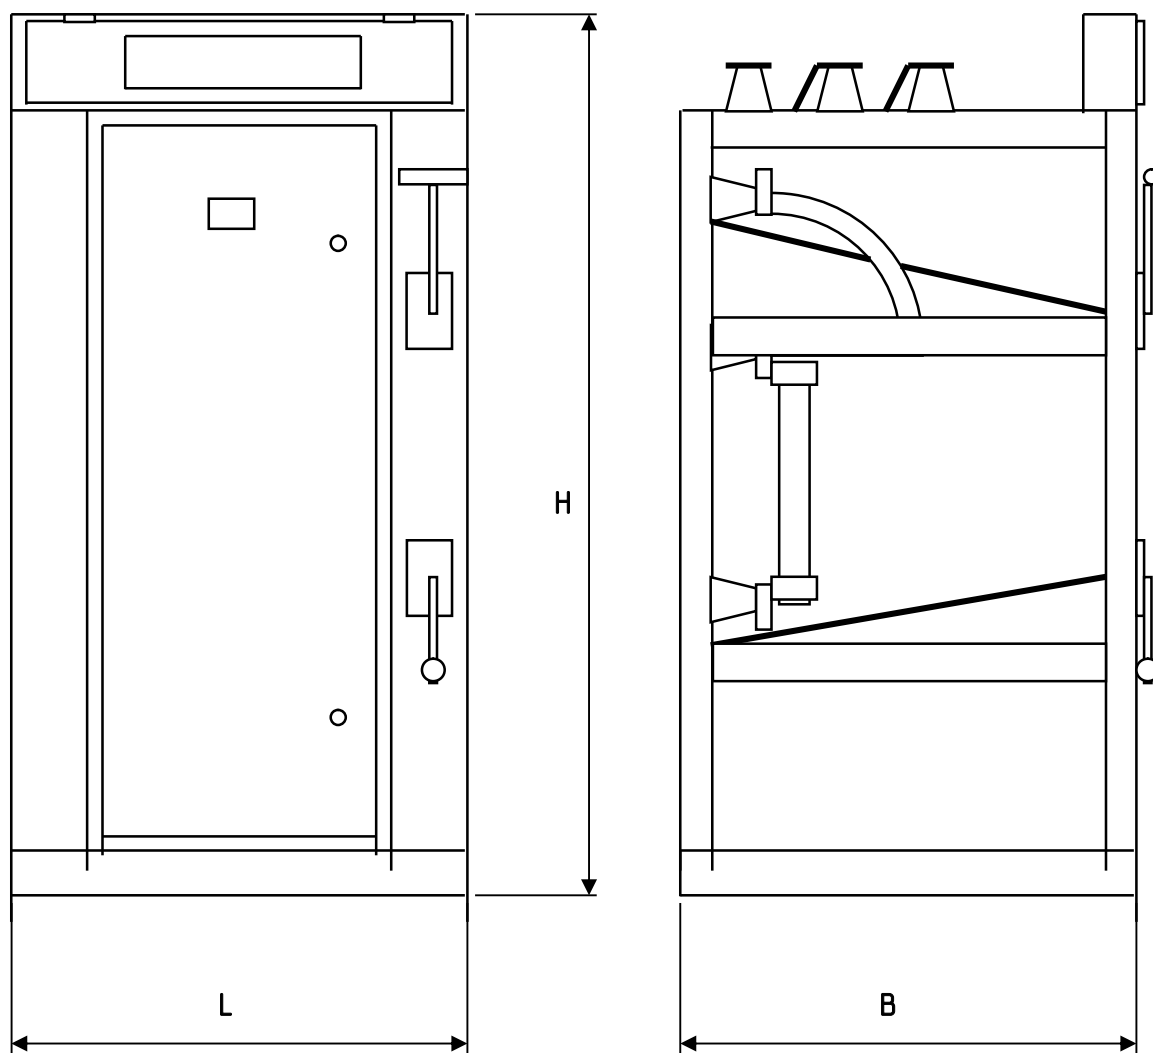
Общий вид и габаритные размеры камер КСО-366, КСО-394
